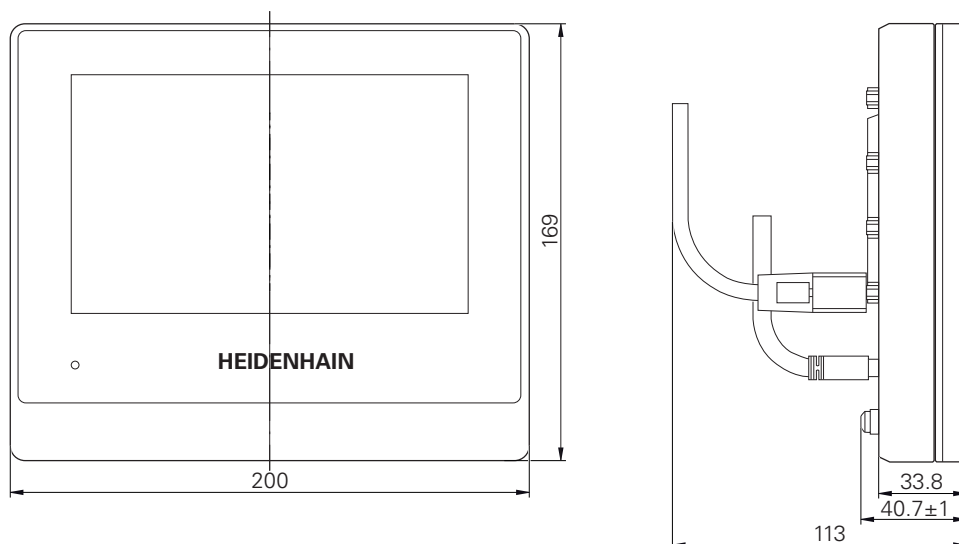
Bemaßungen des Gehäuses der Geräte mit ID 1089178-xx
